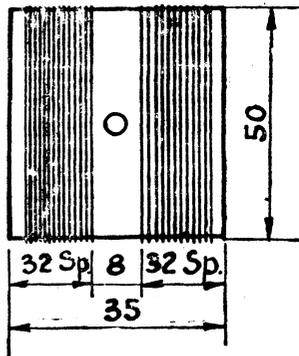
Type de bobinage sur un tube de 50 mm. de diamètre.
